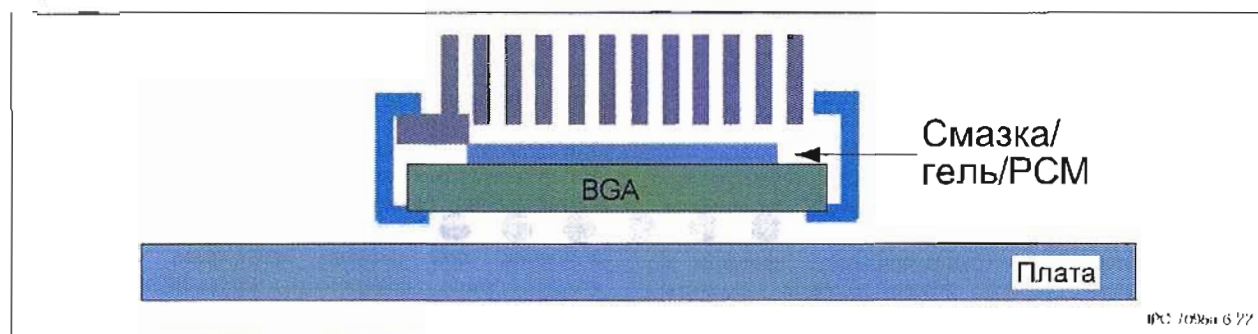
Радиатор, установленный на корпус BGA при помощи зажимов, крепящихся на подложке
